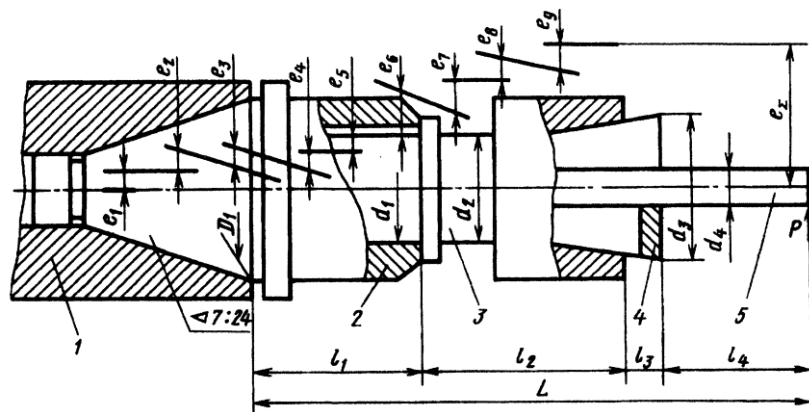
Розмірний ланцюг компоновки допоміжного інструменту
